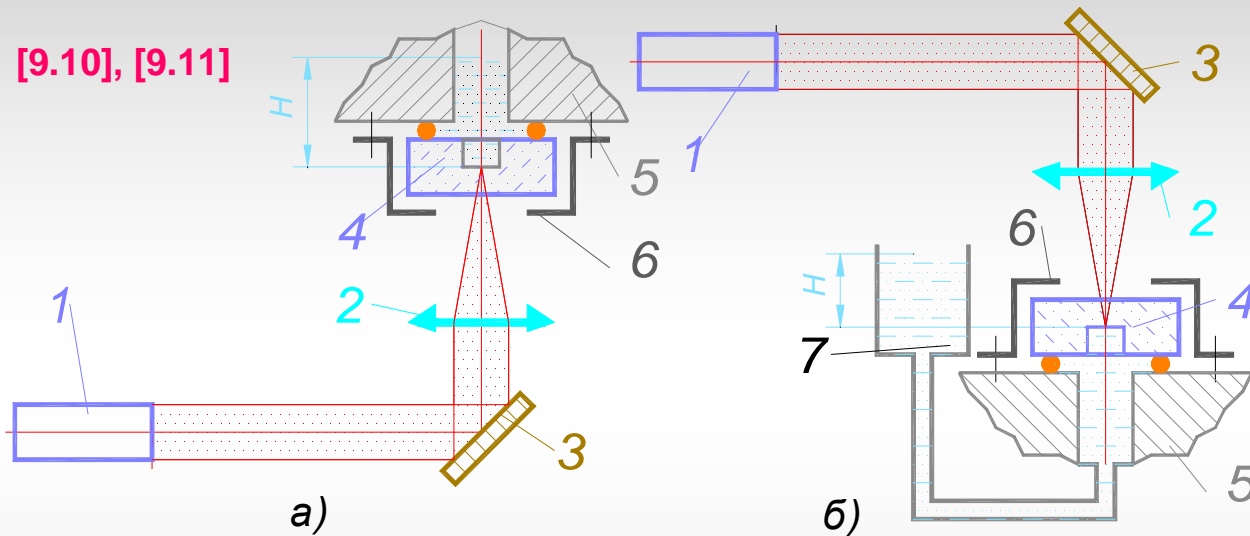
(13.8). Схема обробки отвору з безпервною подачею поглинача до його дна
